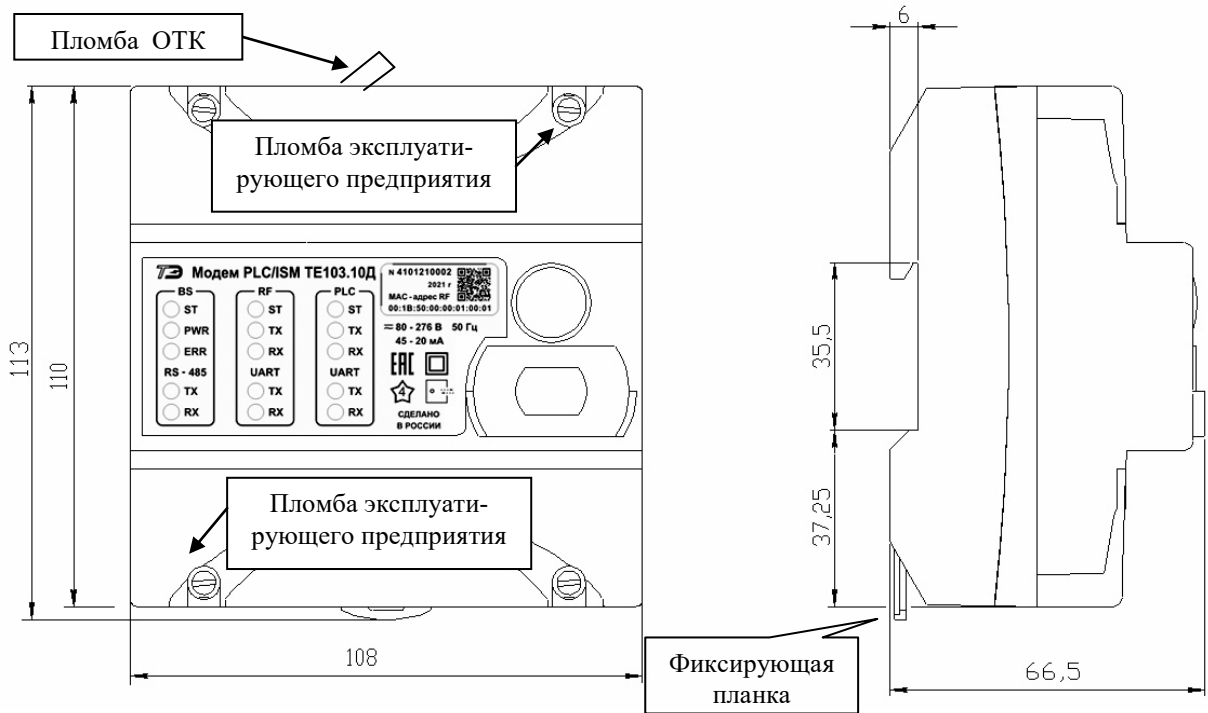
Габаритный чертеж и установочные размеры модемов TE103.10Д, TE103.01Д с защитными крышками
